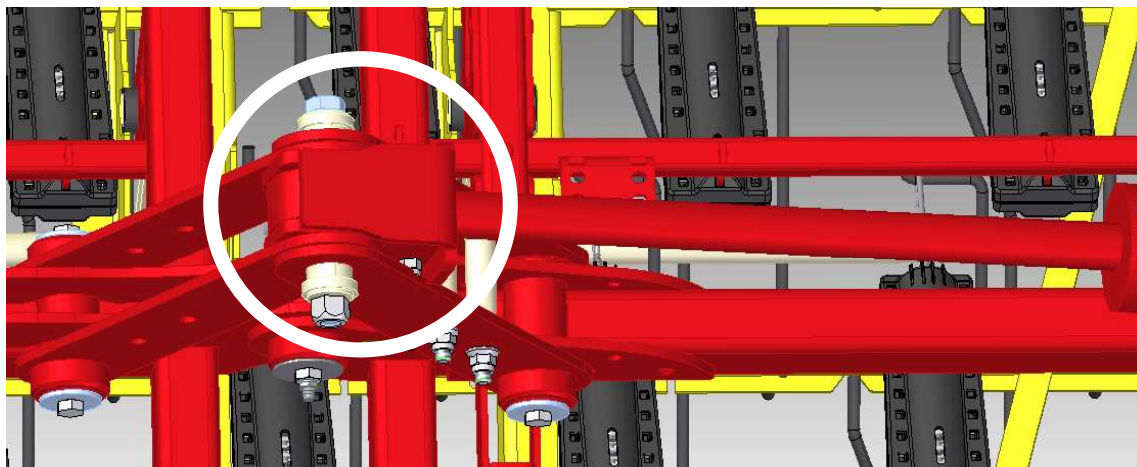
die Begrenzung mittels Bolzen am Zylinderauge montiert
